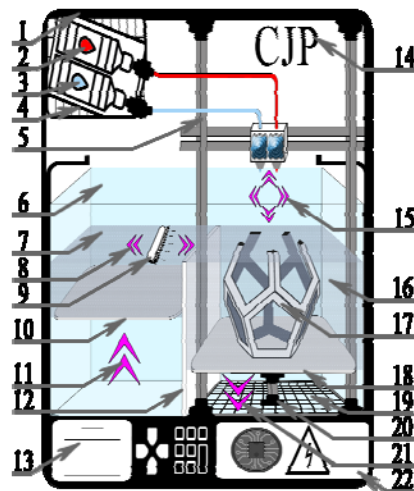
Схема принципу роботи технології 3D друку СДР; 1 – корпус 3D принтера СДР; 2 – витратний матеріал; 3 – витратний матеріал в'яжучої речовини; 4 – герметичний відсік під витратний матеріал; 5 – напрямні платформи побудови та друкарської голівки; 6 – робочий відсік 3D принтера; 7 – камера з витратним матеріалом 3D принтера (кераміка з ВНС); 8 – напрямок щітки нанесення шарів; 9 – щітка нанесення шарів для побудови; 10 – платформа, що подає витратний матеріал; 11 – напрямок руху платформи; 12 – глуха перегородка робочого відсіку; 13 – панель керування 3D принтером; 14 – тип друку 3D принтеру; 15 – напрямок руху друкованої голівки 3D принтера; 16 – камера побудови 3D виробів; 17 – 3D виріб з ВНС; 18 – платформа побудови 3D виробів; 19 – порти для чищення камери побудови; 20 – направляюча платформи побудови; 21 – напрямок руху платформи; 22 – електронна частина 3D принтеру.
